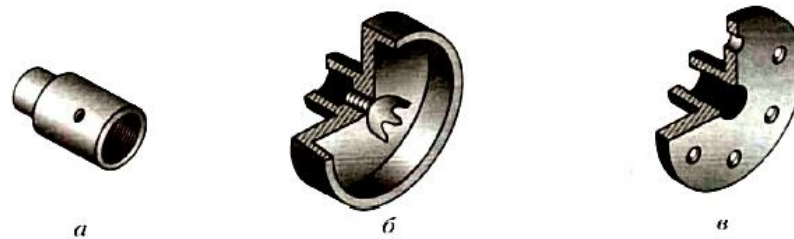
Приспособления для закрепления заготовок: а — патрон; б — трезубец; в — планшайба
